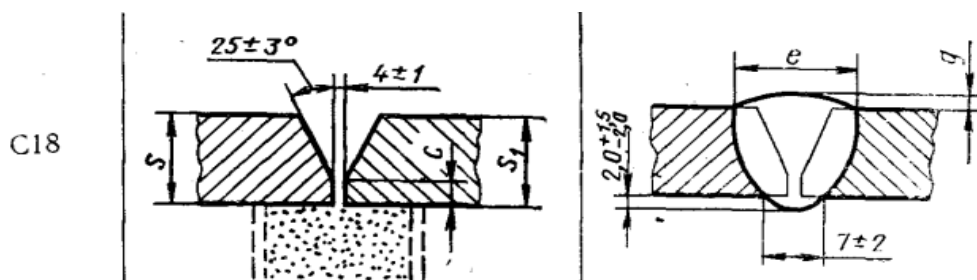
Загальний вигляд стикового зварного з'єднання
